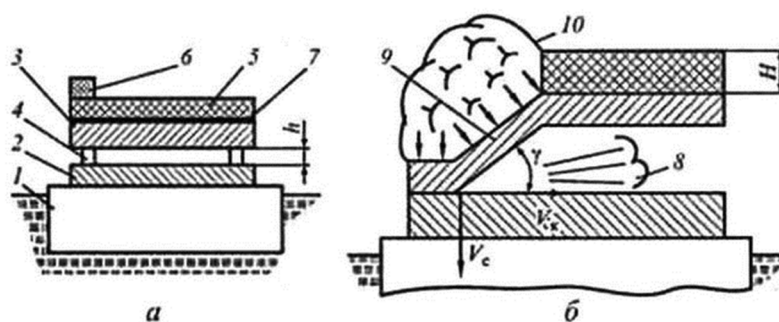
Схема сварки взрывом: а – до начала; б – в процессе взрыва; 1 – жёсткое основание; 2 – неподвижная деталь; 3 – μεταемая деталь; 4 и 7 – прокладки; 5 – заряд; 6 – детонатор; 8 – кумулятивная струя; 9 – детонационная волна; 10 – продукты горения
